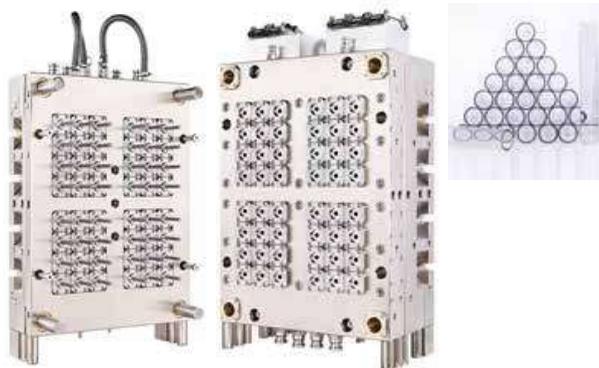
, b, c: molde para tubos de sangre y producto terminado, fabricado en una EcoPower Xpress 160, en versión médica
